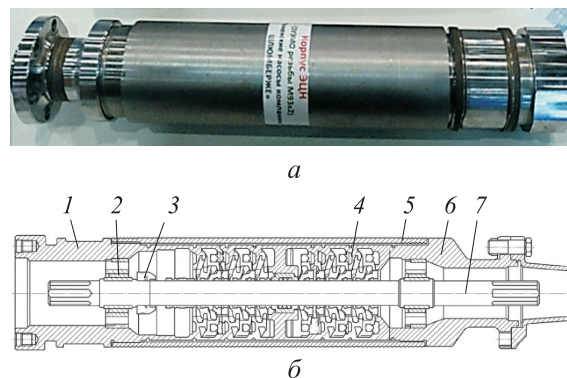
Внешний вид (а) и схема (б) ЭЦН
